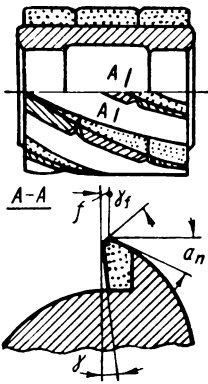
Геометрические параметры режущей части цилиндрической фрезы с винтовыми пластинками из твердого сплава
